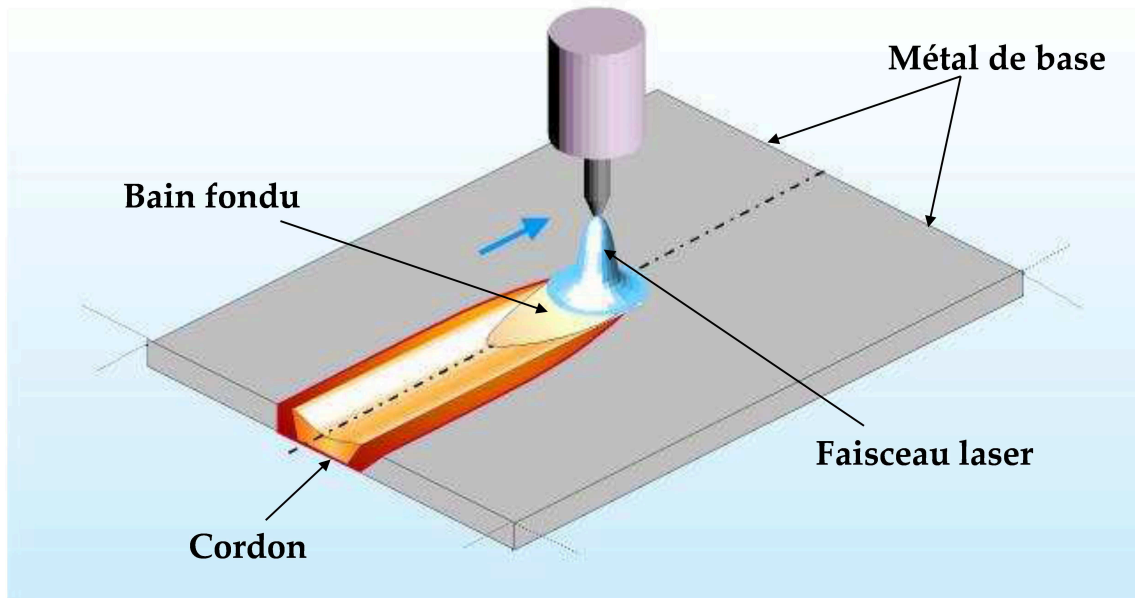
Principe du soudage laser [1].
